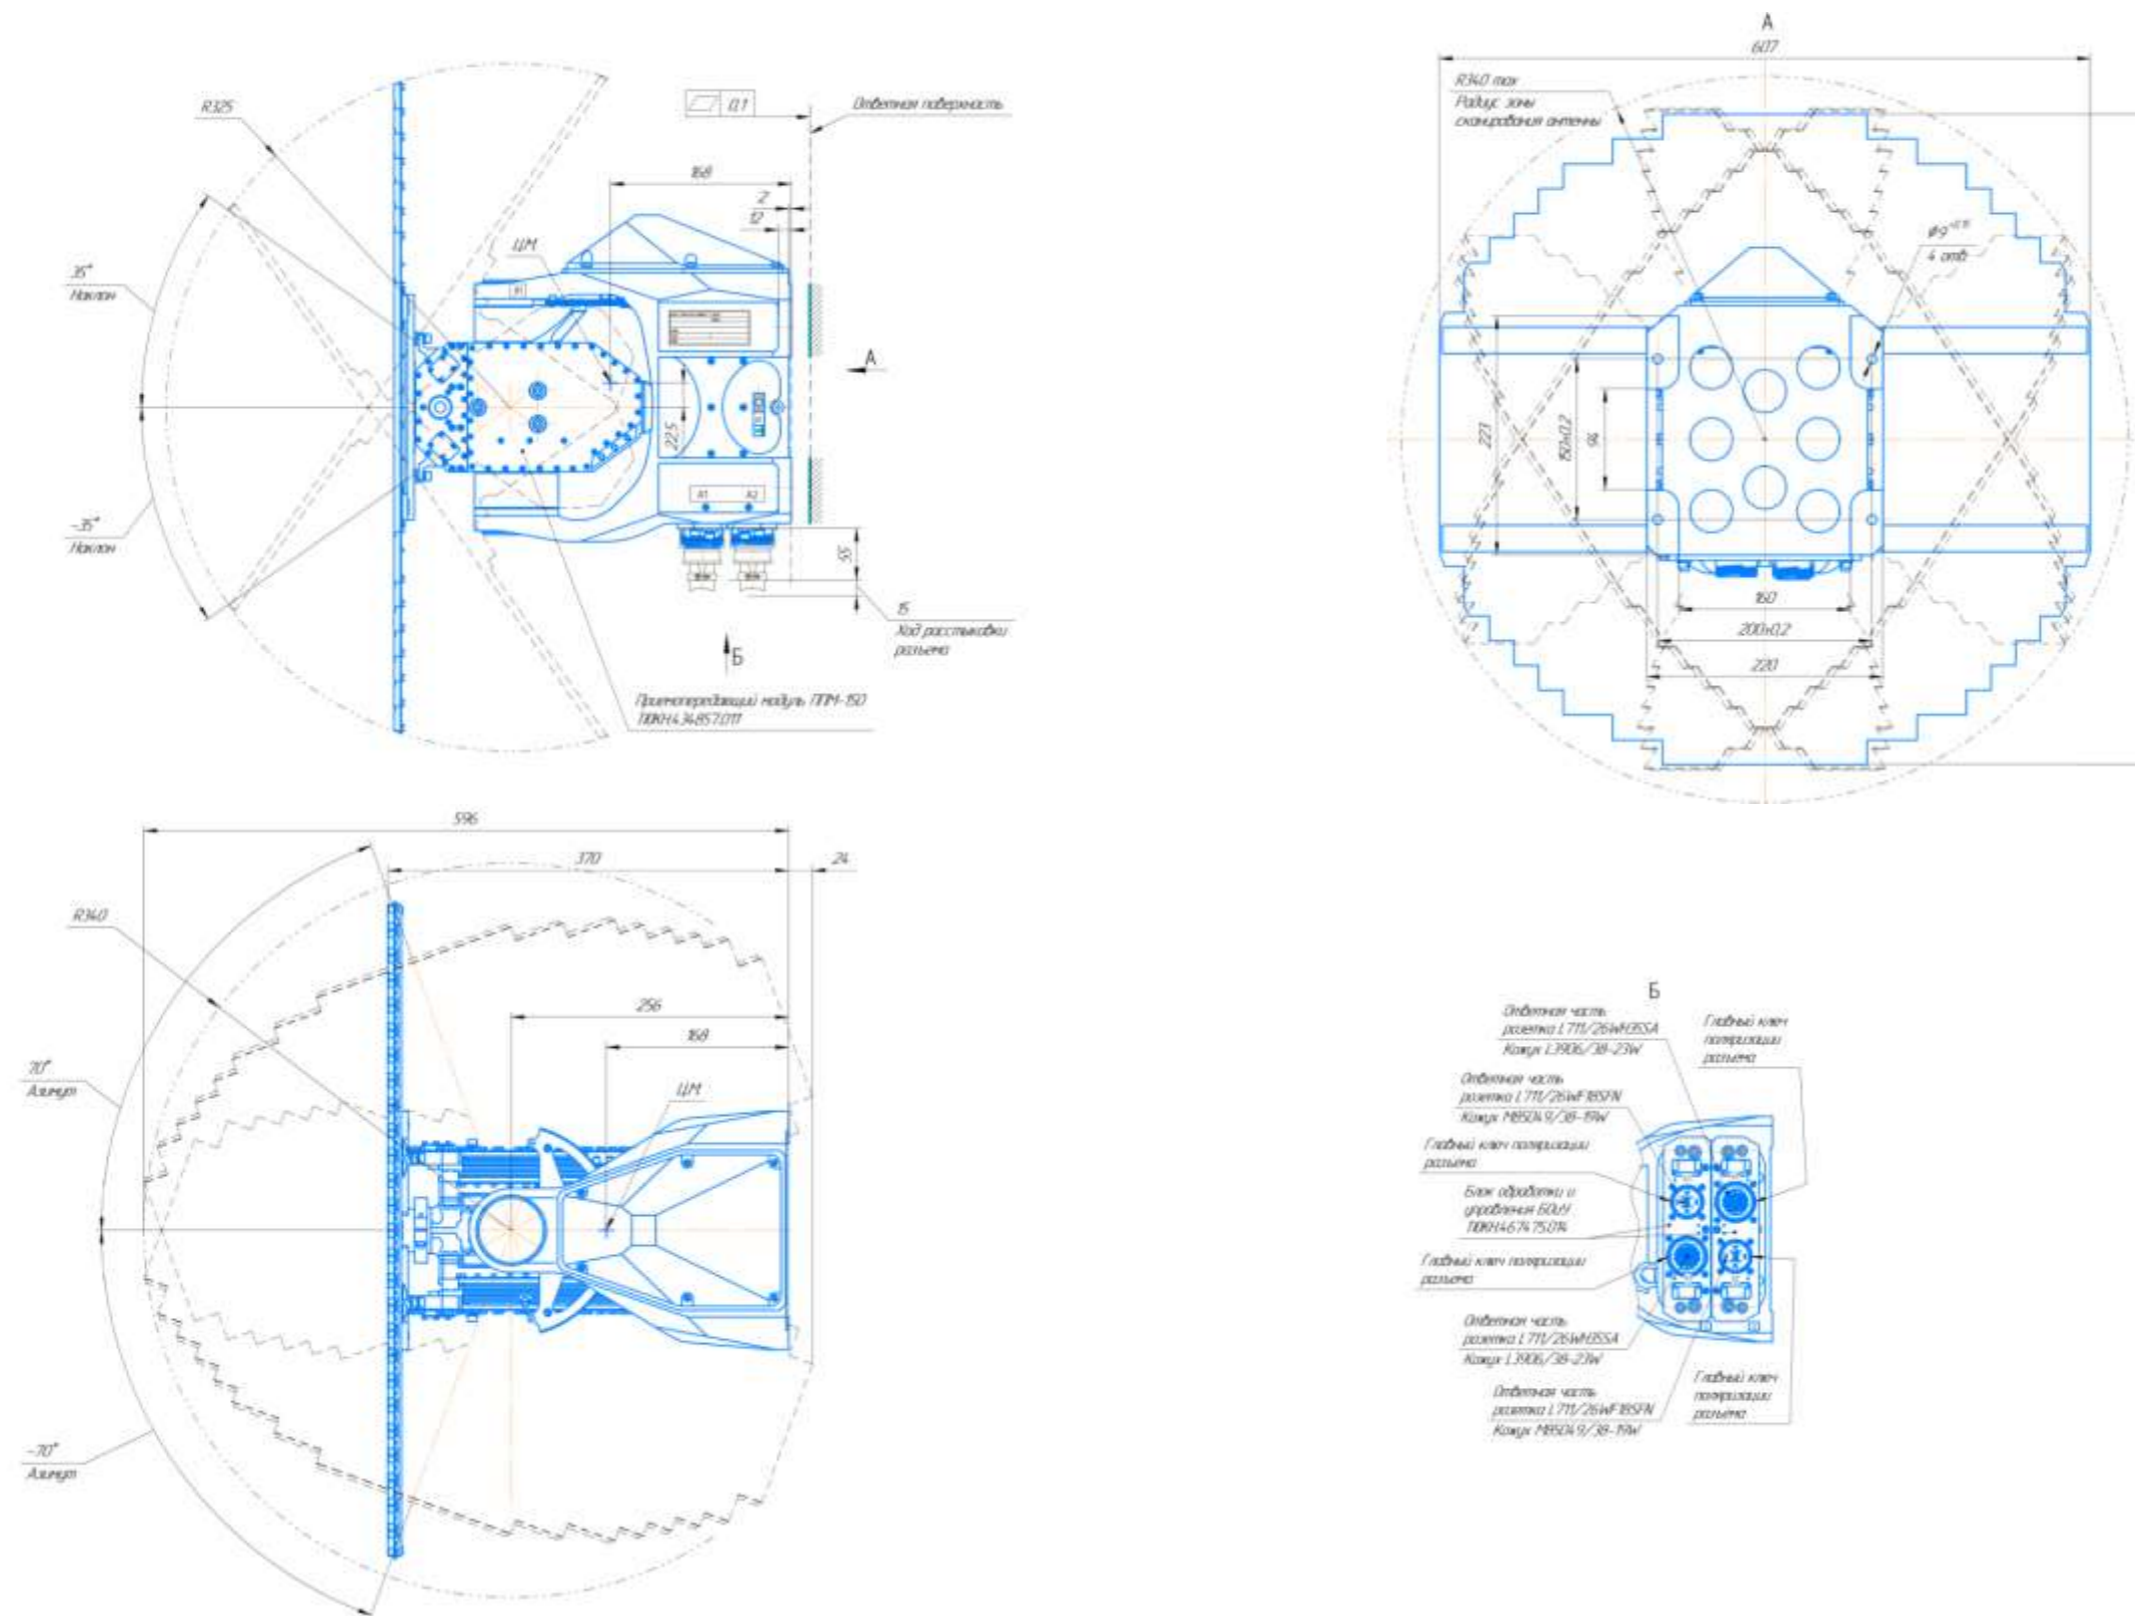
Эскизный чертеж изделия в исполнении 1А813СВ
